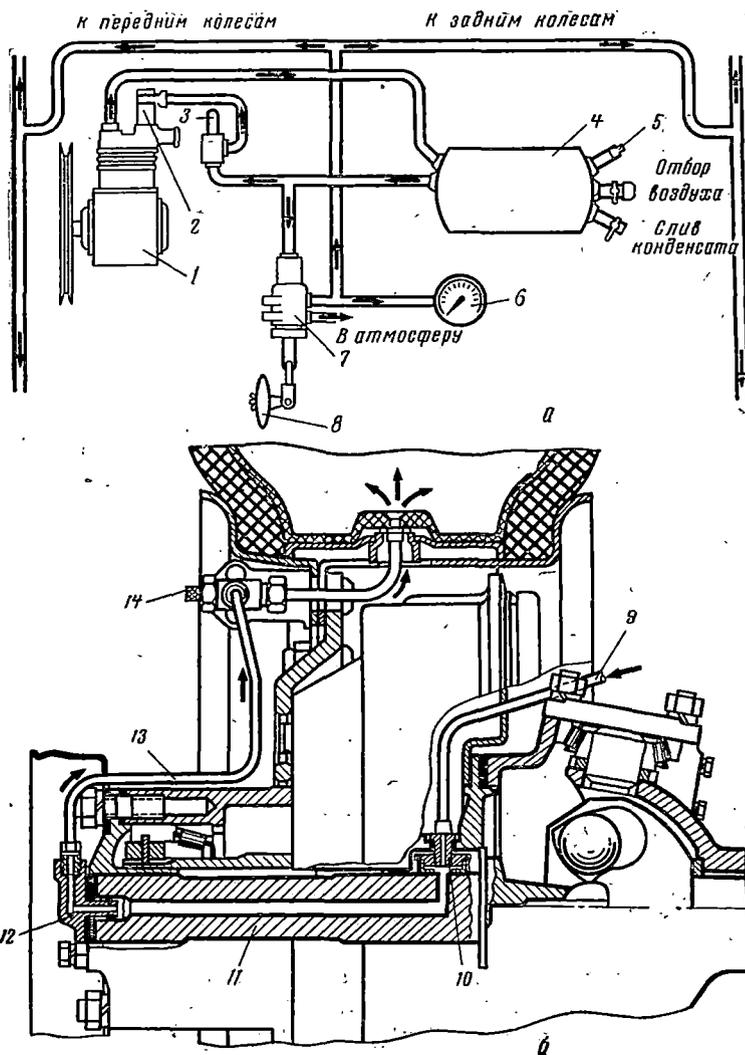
Схема системы шиноподкачивающего устройства *а* и подвода воздуха к шине переднего колеса автомобиля ГАЗ-66, *б*:
